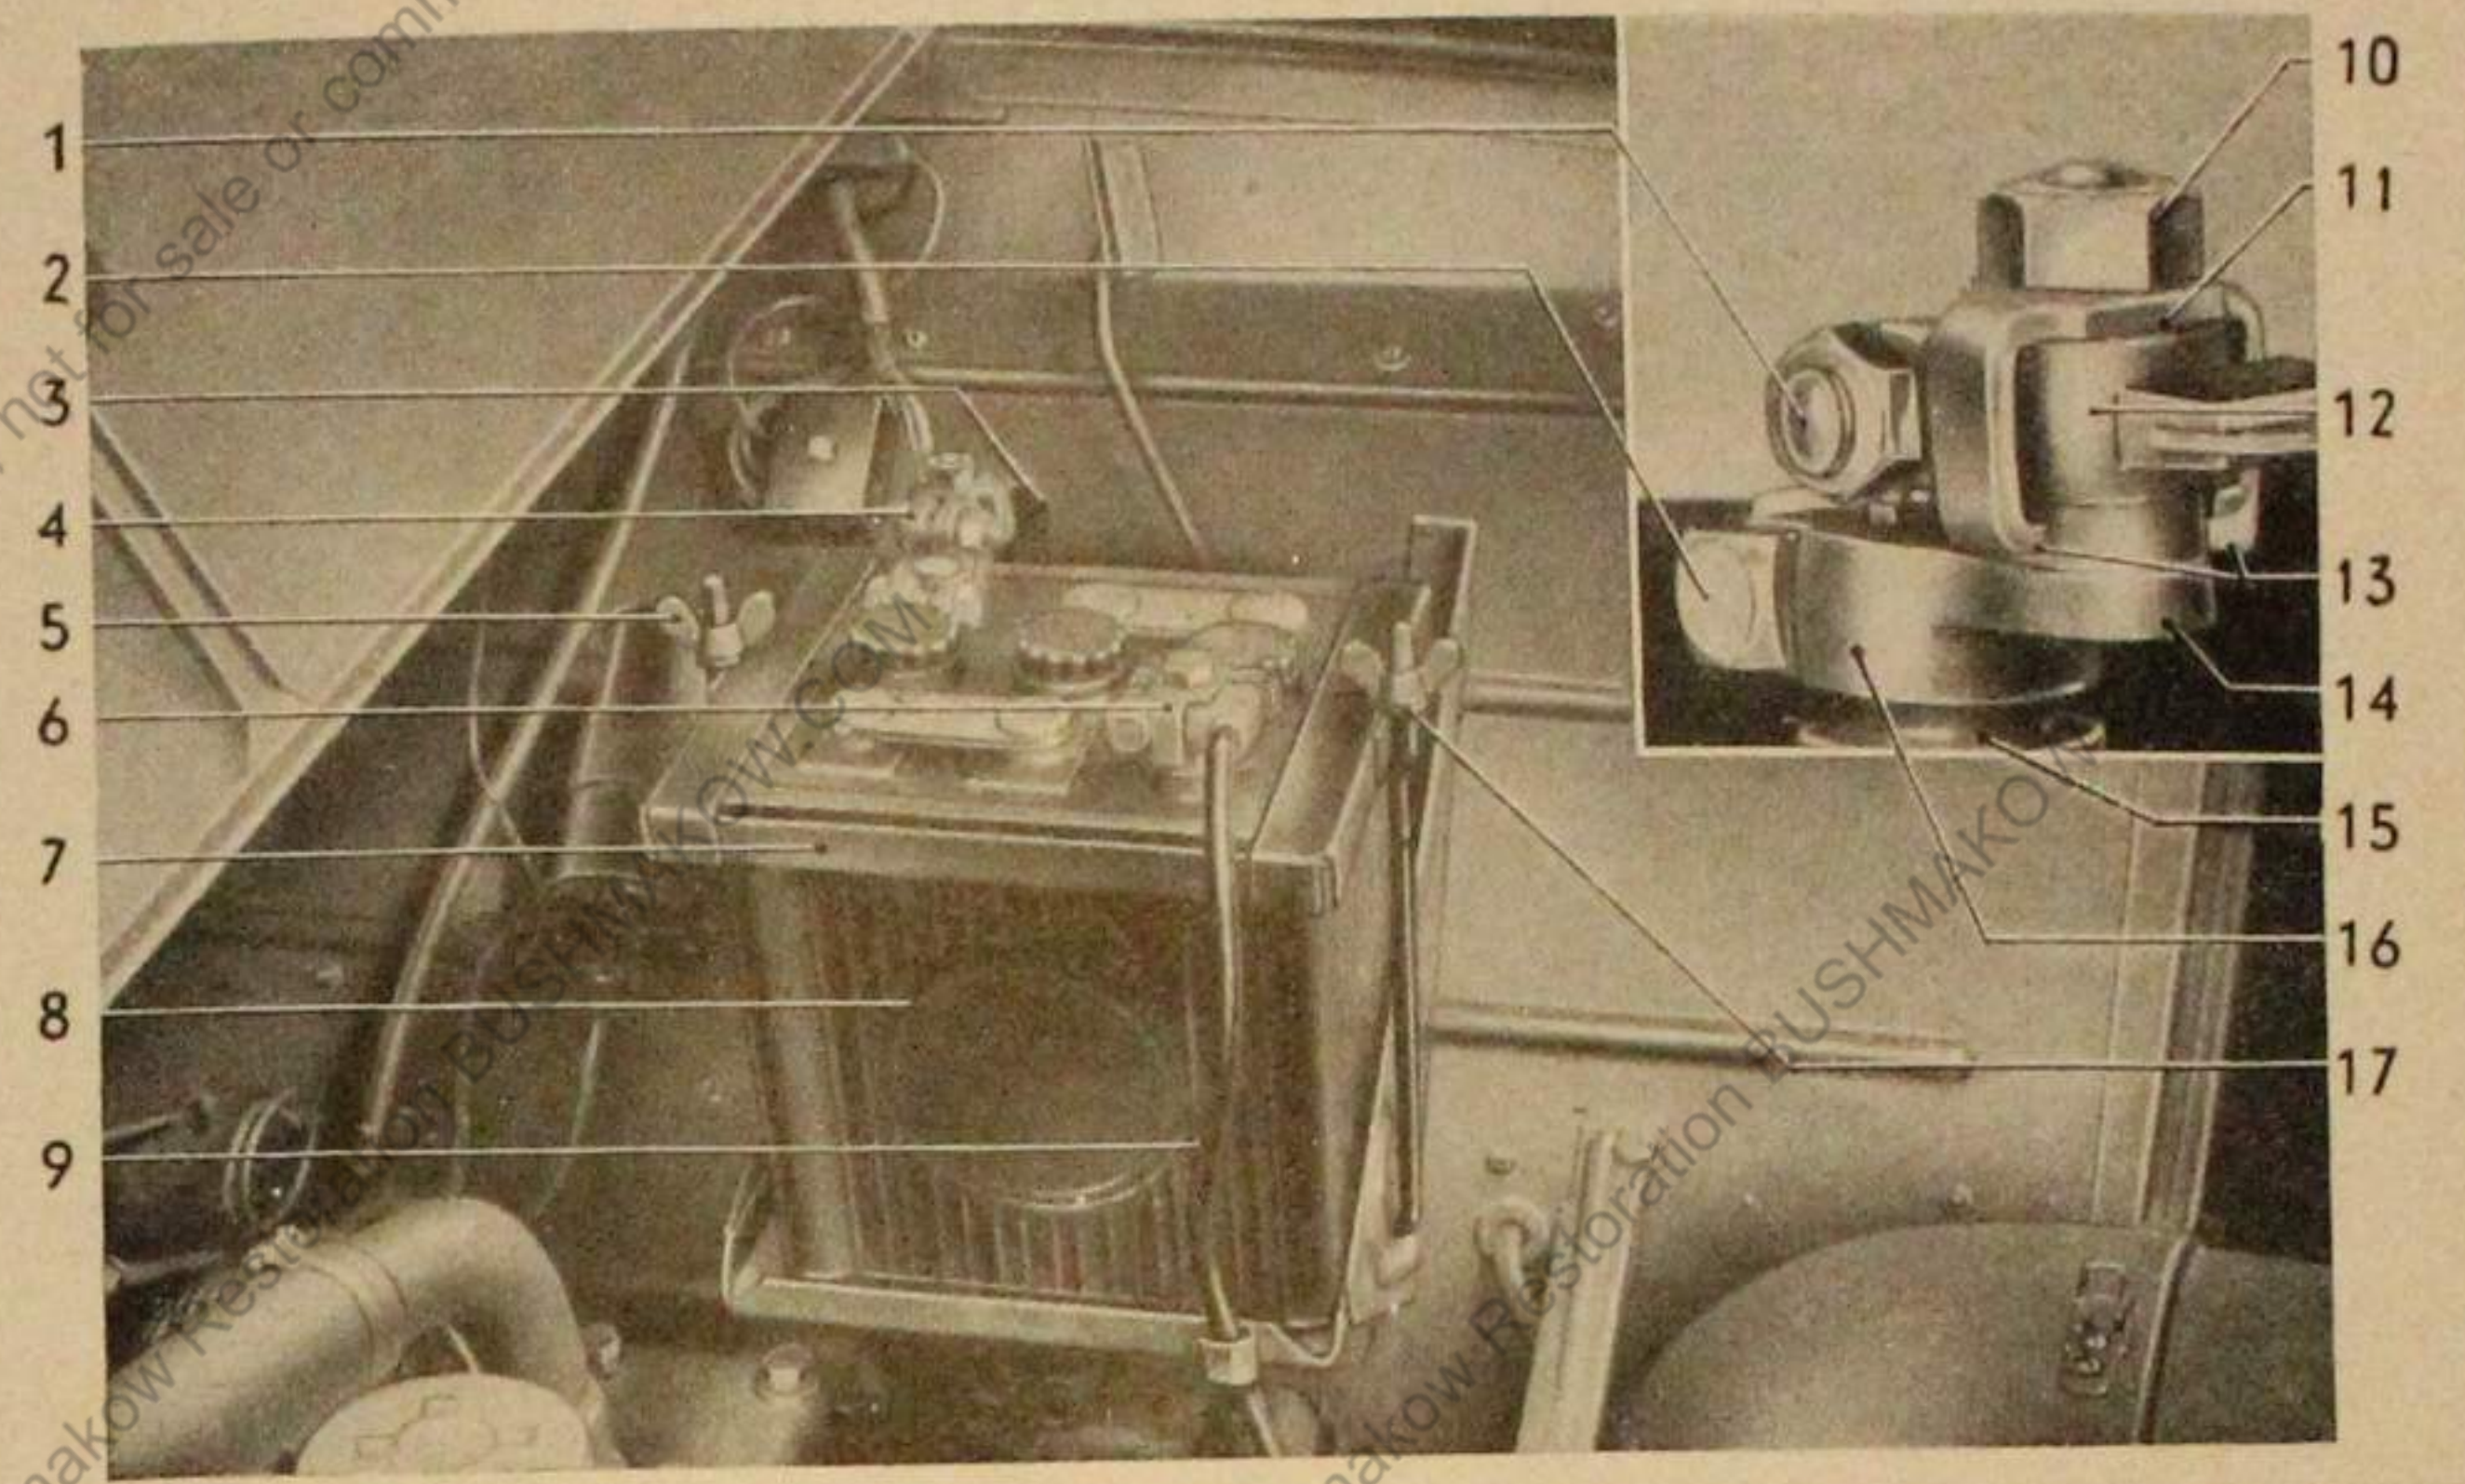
Leicht lösbare Sammlerklemmen eingebaut
